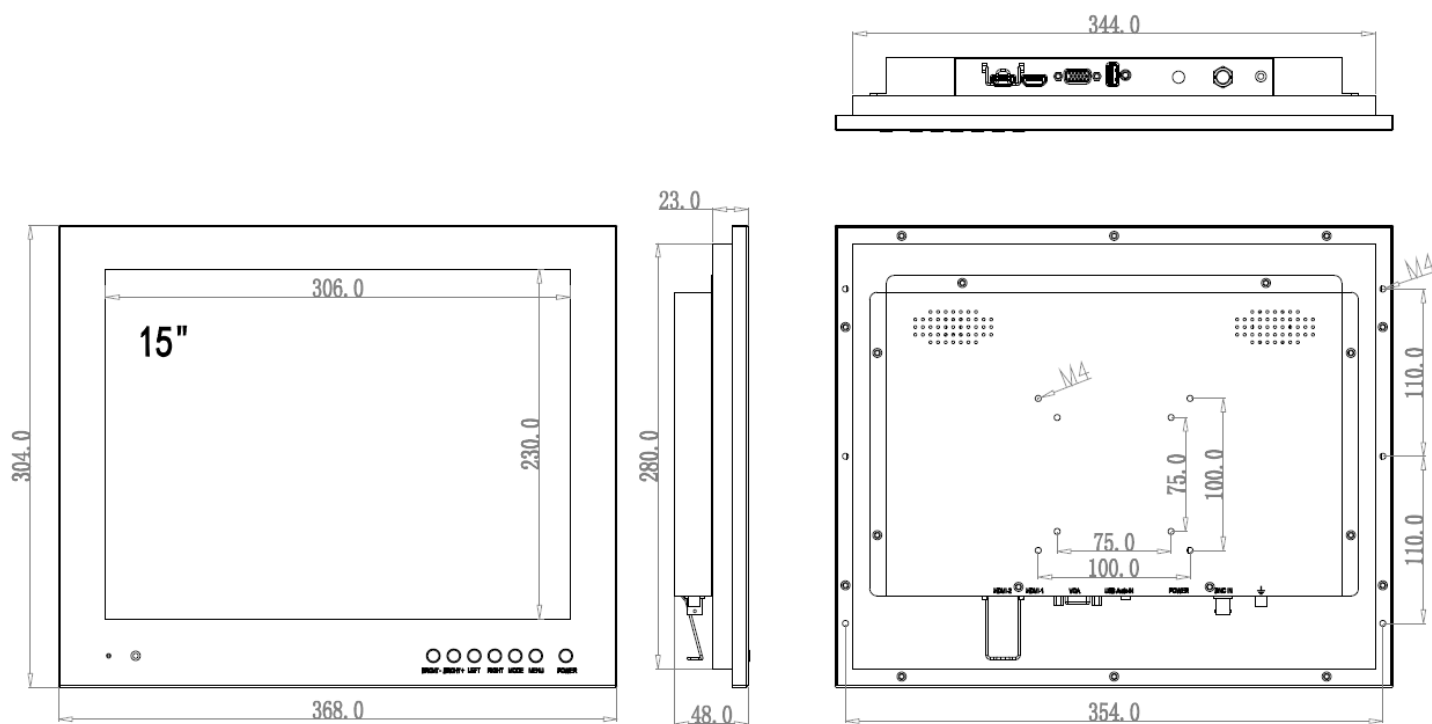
Габаритный чертеж монитора ИВМ-15ЖК.
